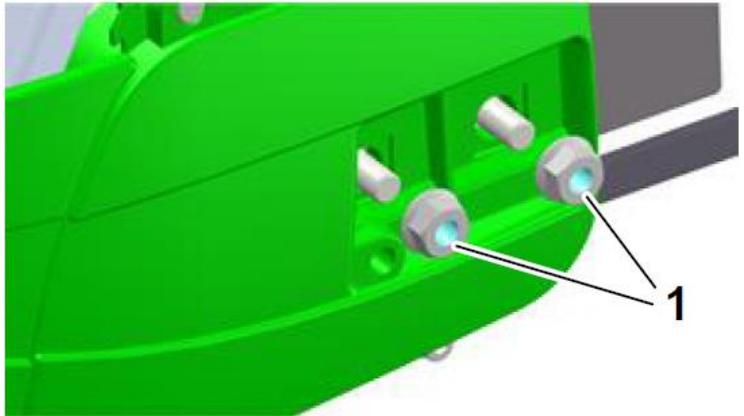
Retrait du couvercle de la courroie trapézoïdale
